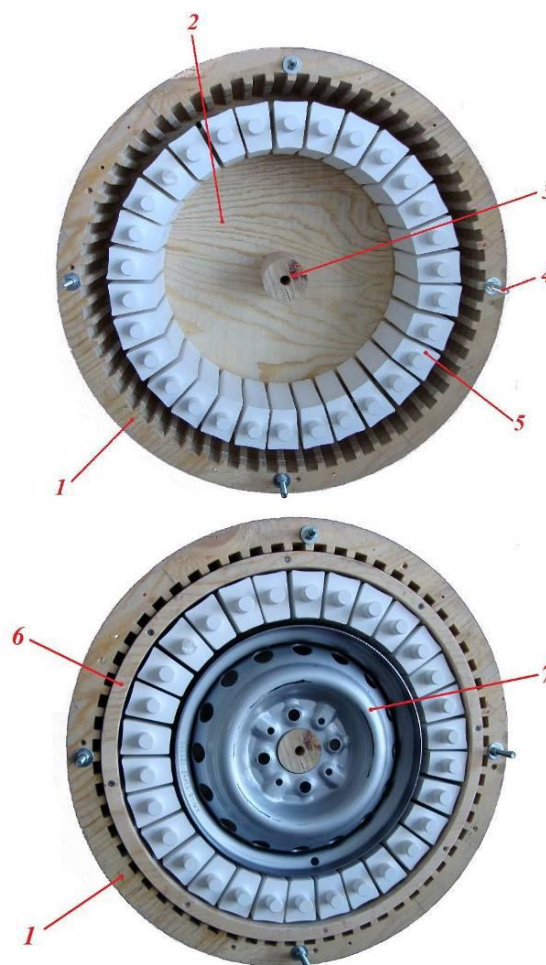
Литейная матрица: 1 – корпус; 2 – днище; 3 – центрирующий цилиндр; 4 – шпильки; 5 – призмы; 6 – кольцо; 7 – колесо дисковое
